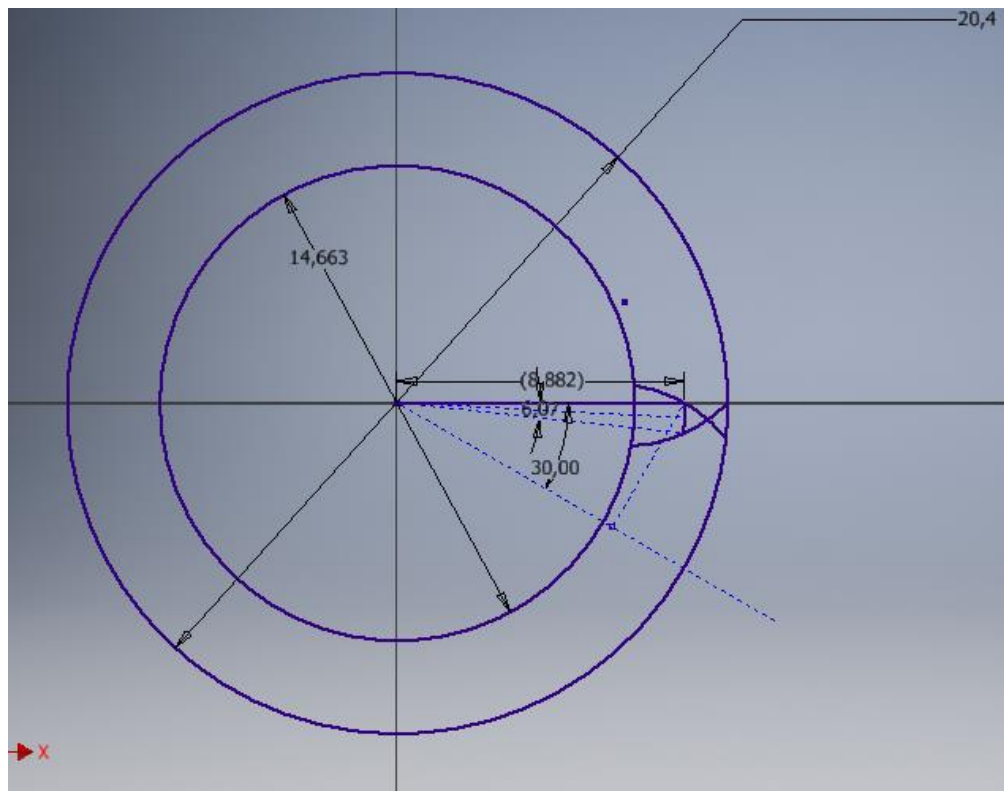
Diseño de engranaje con ángulo de presión de 30° mediante boceto de Inventor
